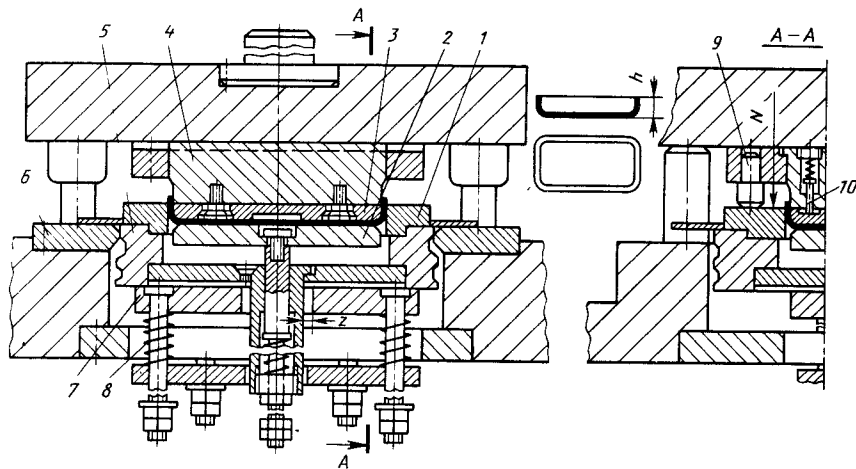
Штмп для обрезки края вертикальных стенок коробок
